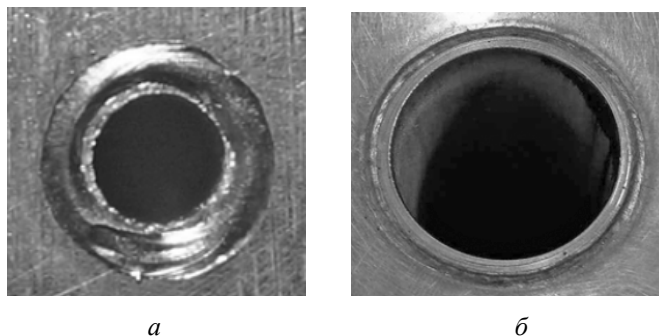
Вид сварного шва, выполненного лазерной сваркой: а) при скорости сварки 1,5 м/мин; б) при скорости сварки 2 м/мин
